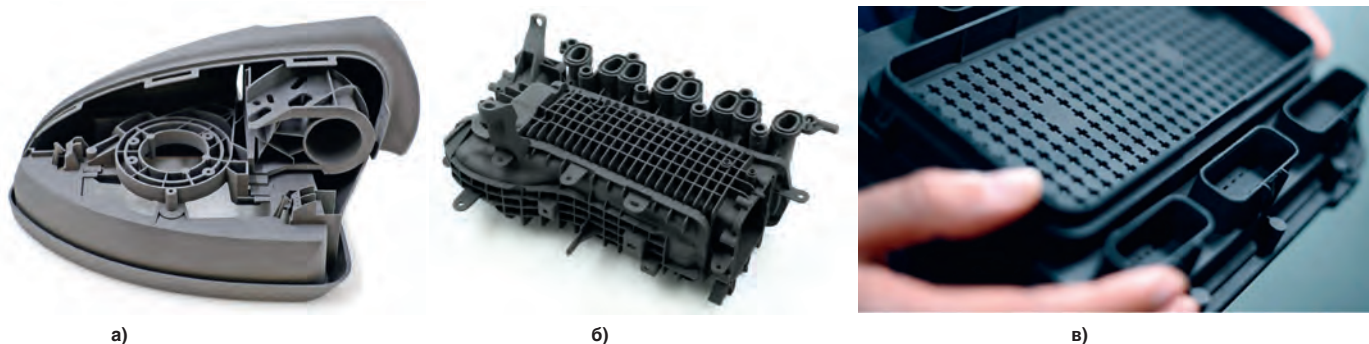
Автомобильные детали из стеклонаполненного полиамида: а — корпус зеркала заднего вида, б — впускной коллектор двигателя, в — автомобильный блок предохранителей для проверки легковых
